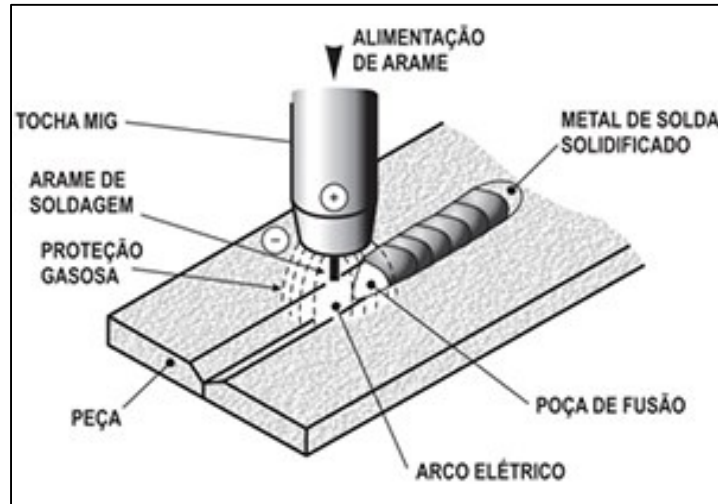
Processo de Soldagem MIG/MAG Fonte: ESAB
